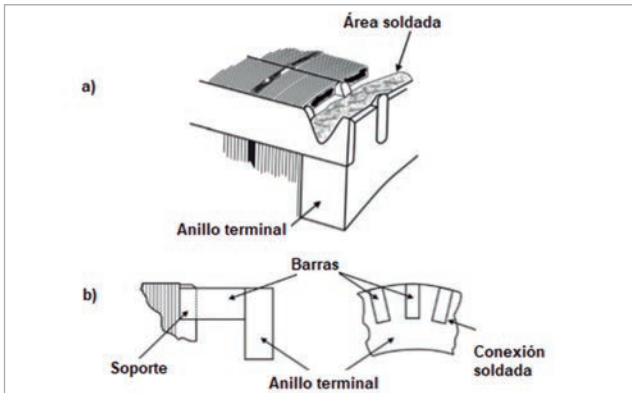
a) y b) Detalles de la construcción de un rotor jaula de ardilla con barras soldadas.
